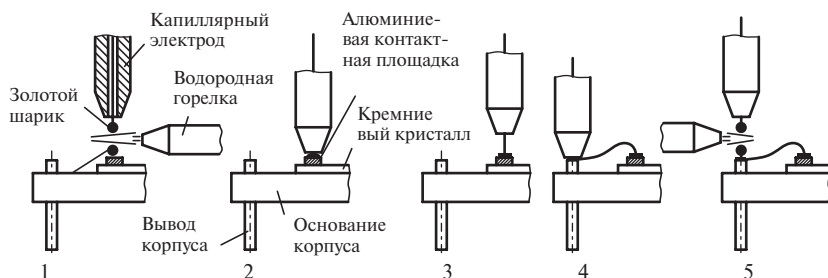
Схема процесса микросварки: 1 — оплавливание золотой проволоочки с образованием шарика; 2 — присоединение проволоочки к контактной площадке кристалла; 3 — подъем капиллярного электрода; 4 — присоединение проволоочки к внешнему выводу корпуса; 5 — подъем электрода и оплавливание проволоочки
